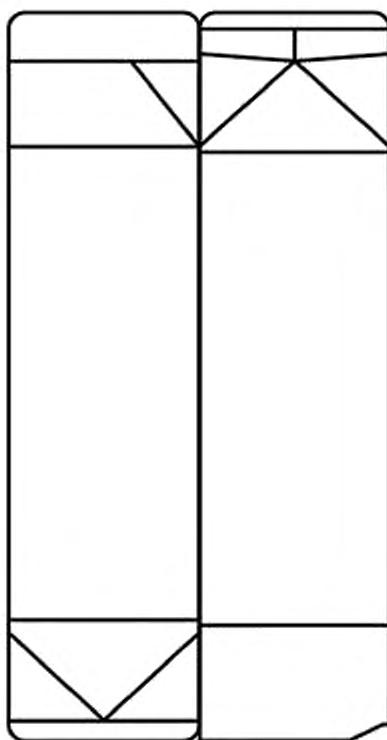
Заготовка коробки — высечка с нанесенными линиями сгиба (биговкой) и продольным сварным швом
